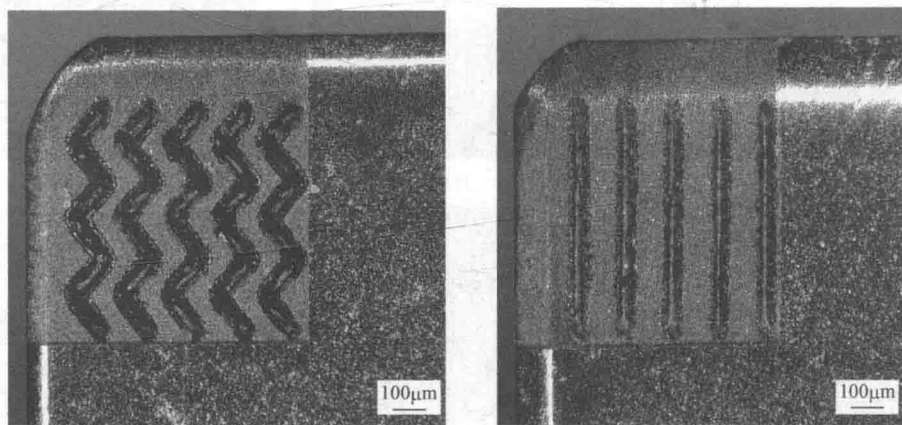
陶瓷刀具表面激光加工的微纳复合织构形貌
